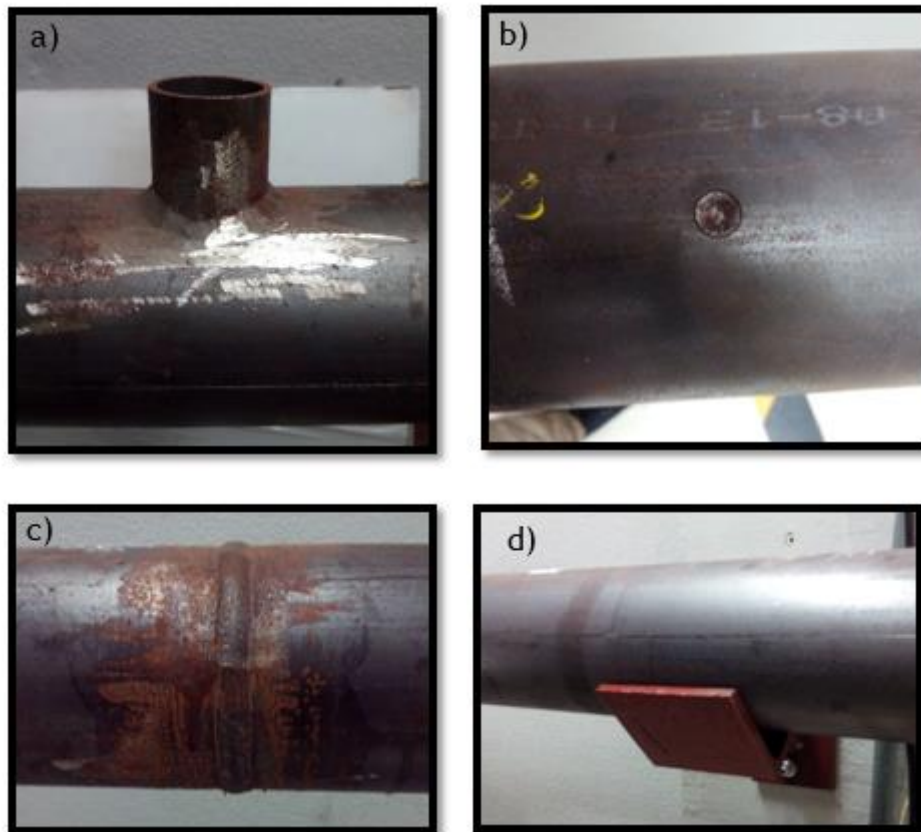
Fotografias das zonas do tubo que podem gerar sinais nas ondas guiadas. a) tubo soldado, b) furo não passante, c) soldadura, d) suporte.
